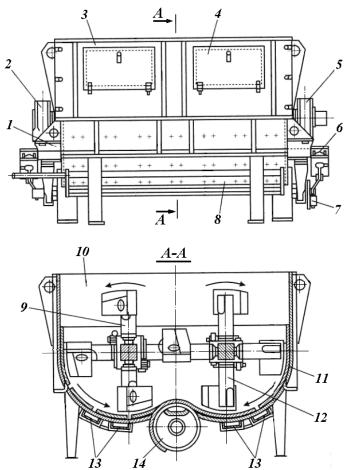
Лопастной асфальтосмеситель периодического действия: 1 - рама; 2, 5 – корпуса подшипников; 3, 10 – соответственно боковая и торцевая стенки; 4 – крышка; 6 – пневмоцилиндр управления затвором; 7 – конечный выключатель; 8 – корпус; 9, 12 – лопастный вал; 11 – футеровка; 13 – теплообменные рубашки; 14 – секторный затвор
